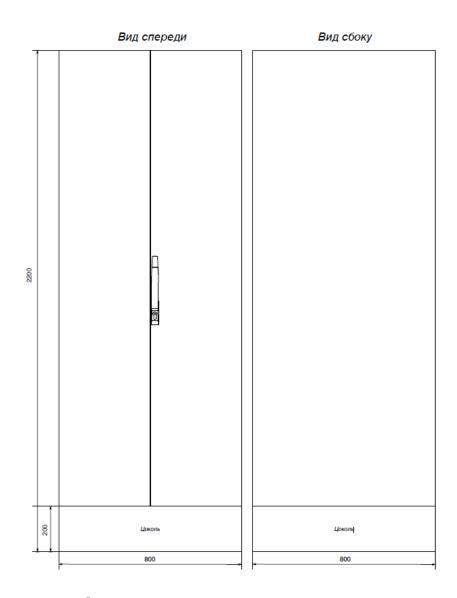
Внешний вид и габаритные размеры концентратора с двухстворчатыми дверями
